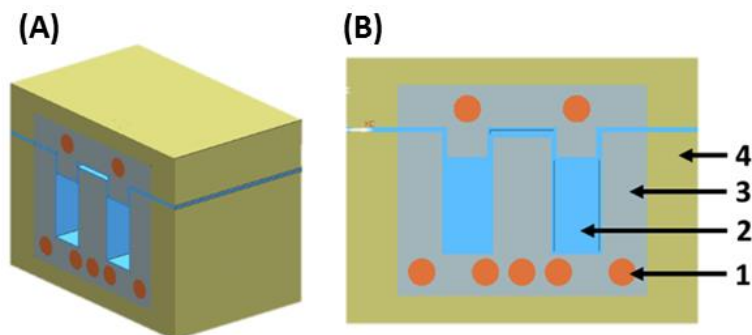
Molde diseñado sin barrera térmica. (A) Vista seccional isométrica del molde; (B) Vista seccional frontal del molde, 1: tubería de cobre, 2: Fundas de silicona, 3: compuesto GSS/EP, 4: compuesto SMC/EP.
